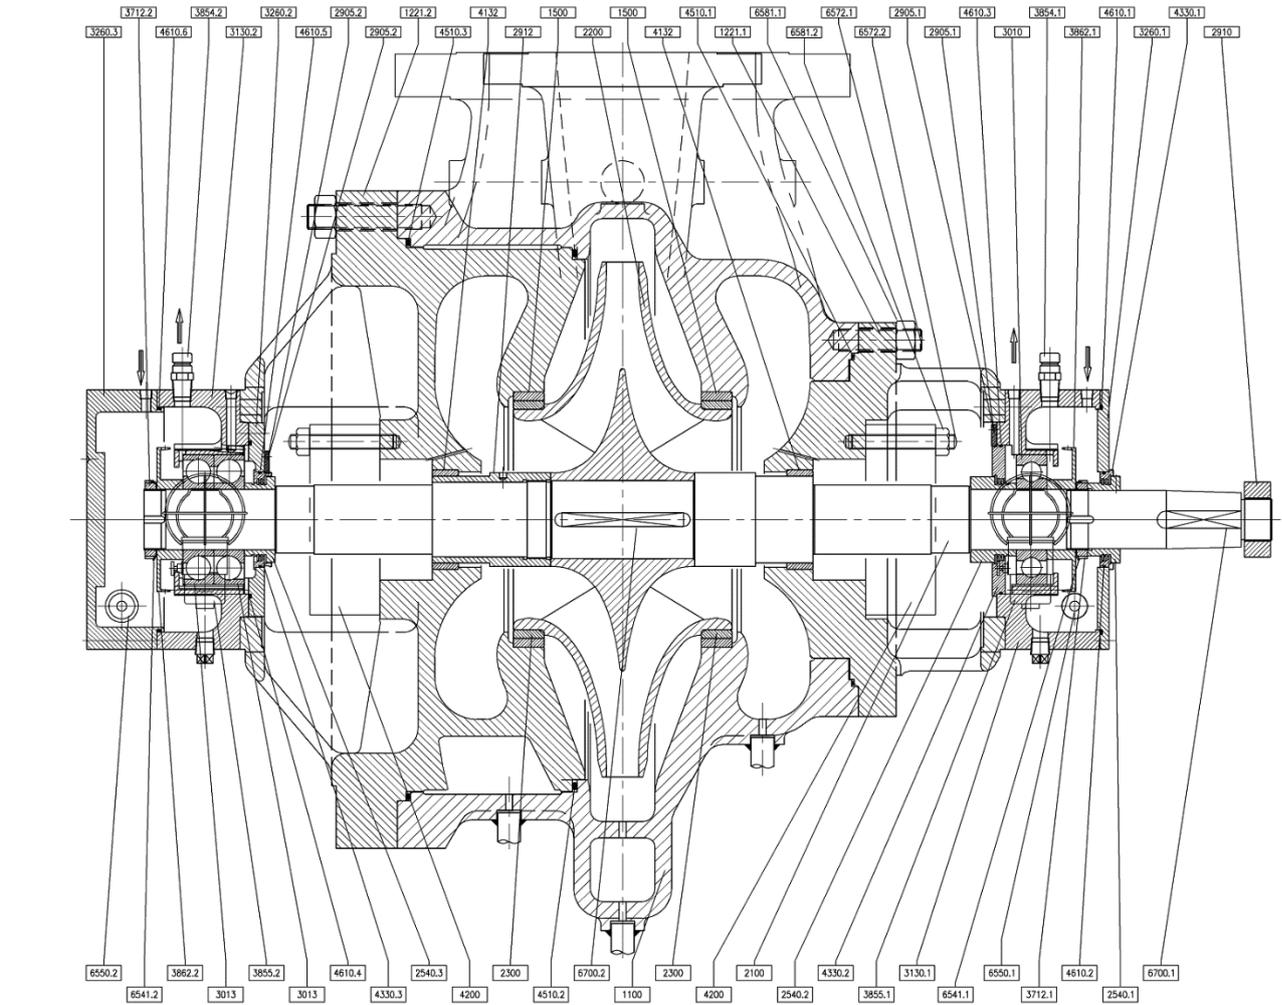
Dessin d'ensemble en coupe de la pompe centrifuge 100-PM113
